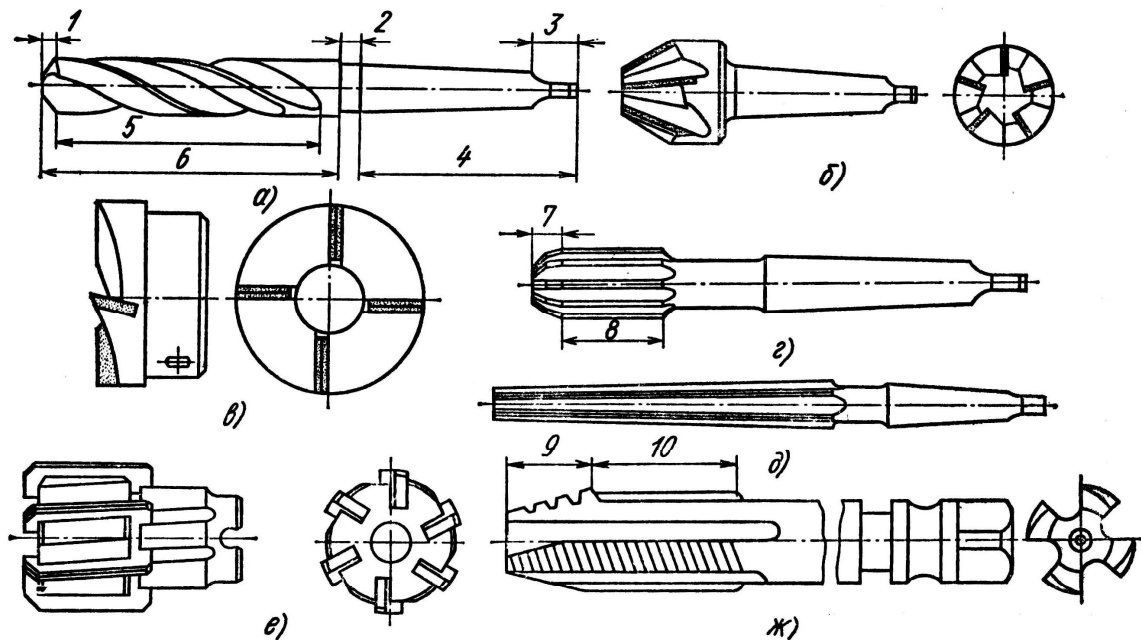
Види основних різальних інструментів, які застосовуються на свердлильних верстатах.
